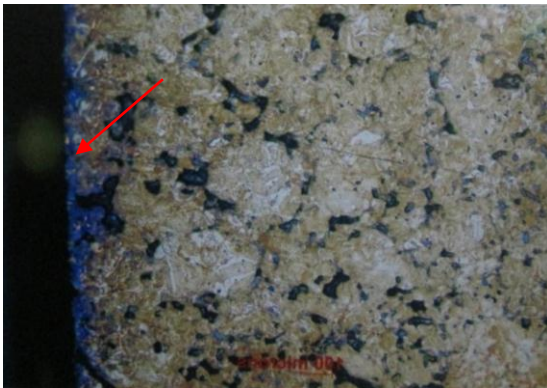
Cacat Pada Rod Akibat Kontak Arus listrik Welding
